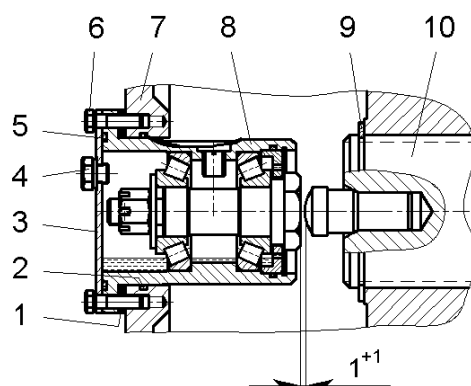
Регулировка зазора упора солнечной шестерни:
